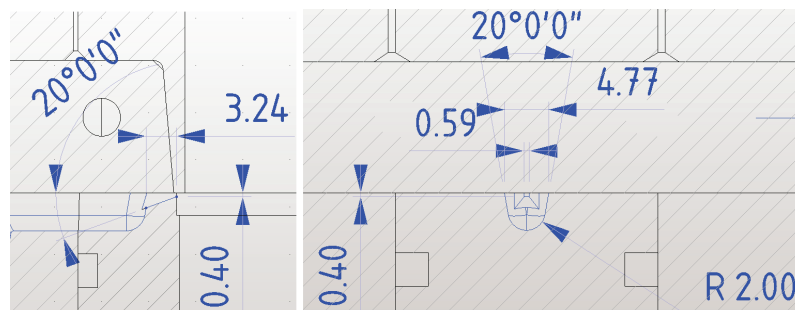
Pormenor do ataque à junta em corte longitudinal (à esquerda) e transversal (à direita) (retirado do 2D).
